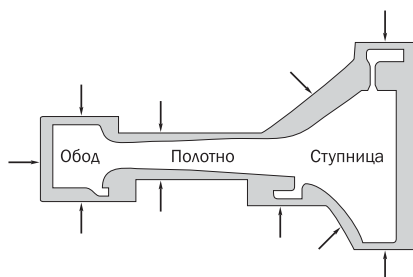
Направления прозвучивания заготовки диска турбины 1-й ступени
